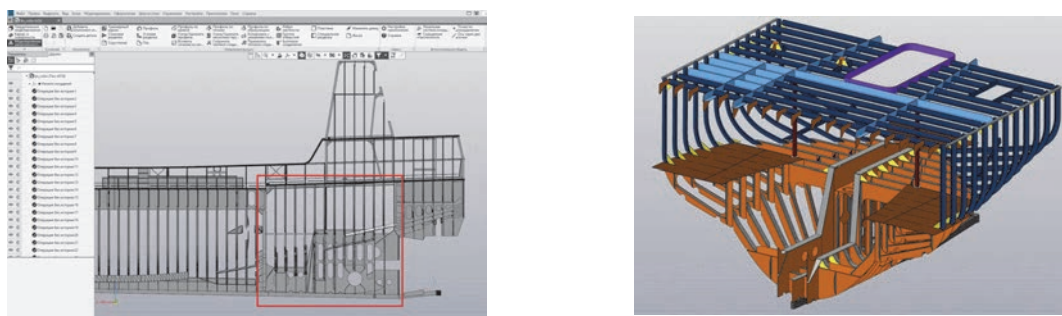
Моделирование фрагмента корпуса нефтесборщика
